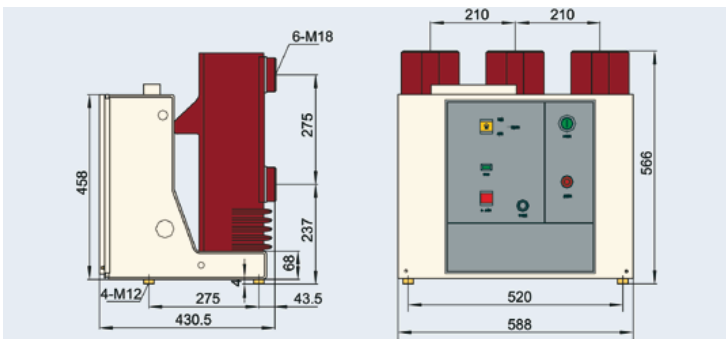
Внешний вид и монтажные размеры выключателя ZN63A-12/T - 31.5
